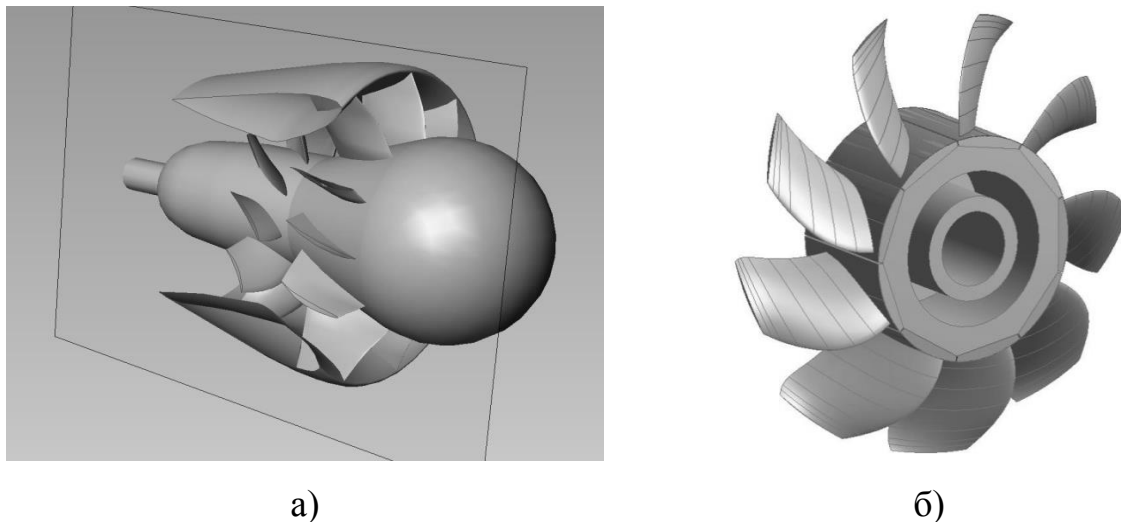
Конструкция а) водометного движителя и б) его рабочего колеса
